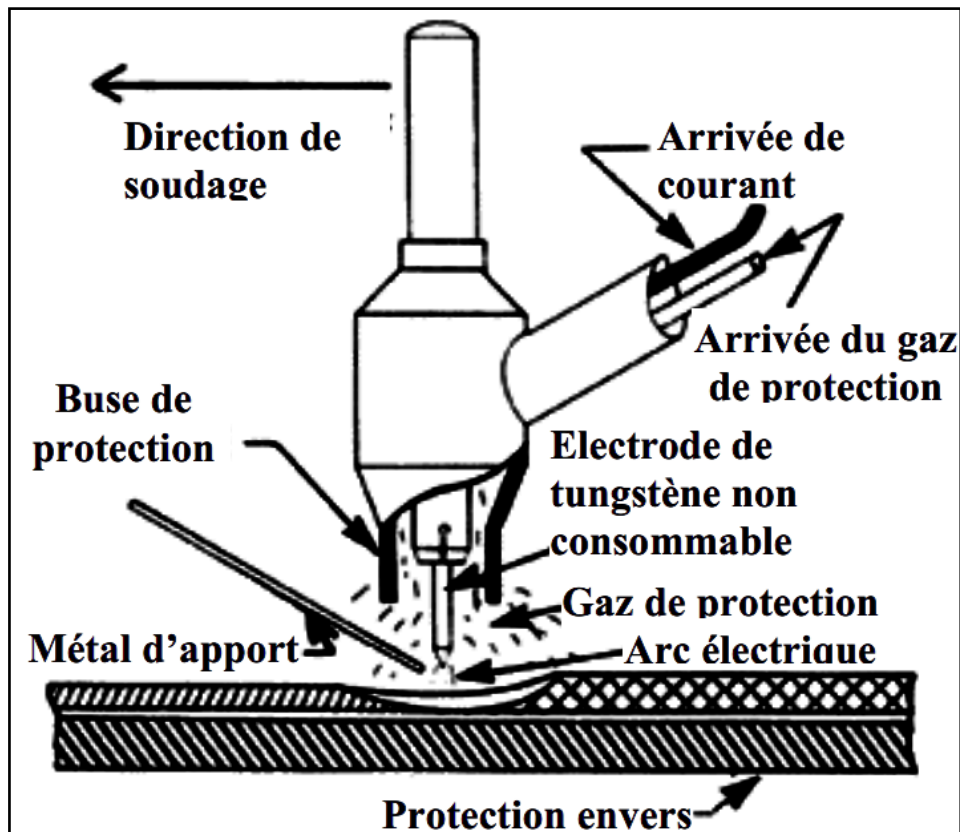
Torche TIG et son procédé de soudage [3].
